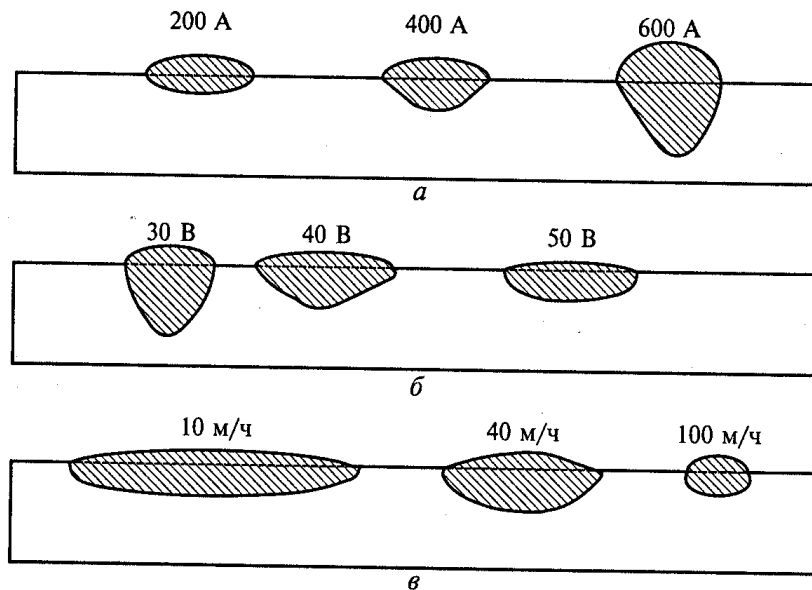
Вплив на форму шва параметрів режиму зварювання: а – зварювальний струм, б – напруга дуги, в – швидкість зварювання
